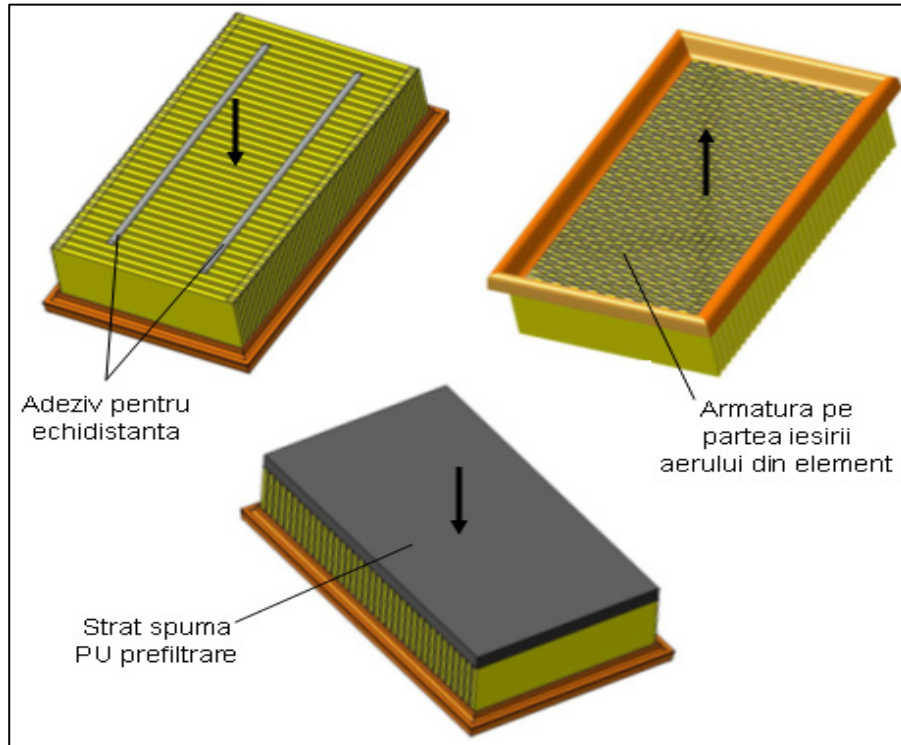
Construcția elementelor de aer de tip plat [104]
